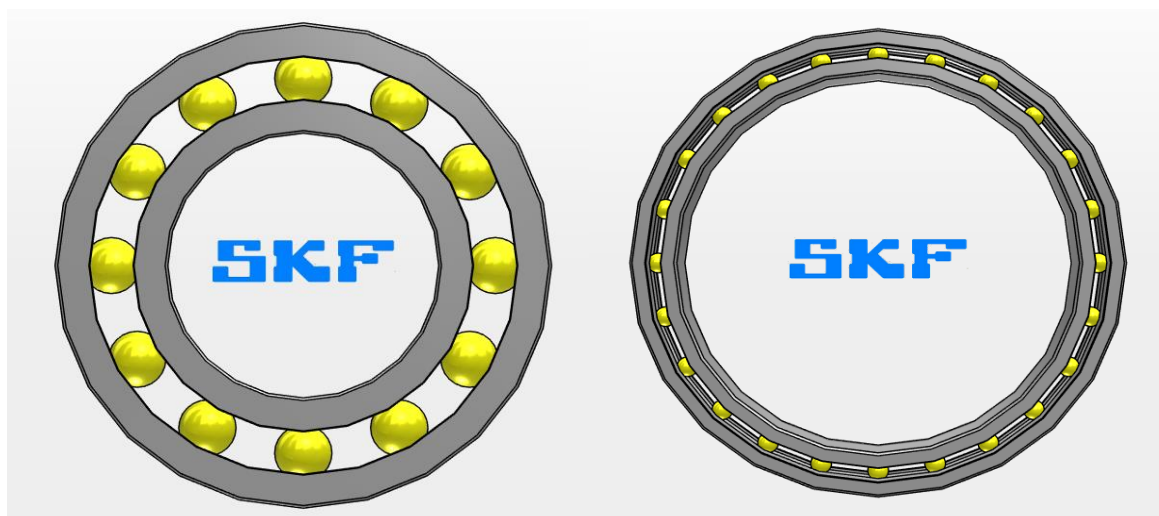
Imagen 3D de los rodamientos 16006 (izquierda) y W 61706 (derecha)
